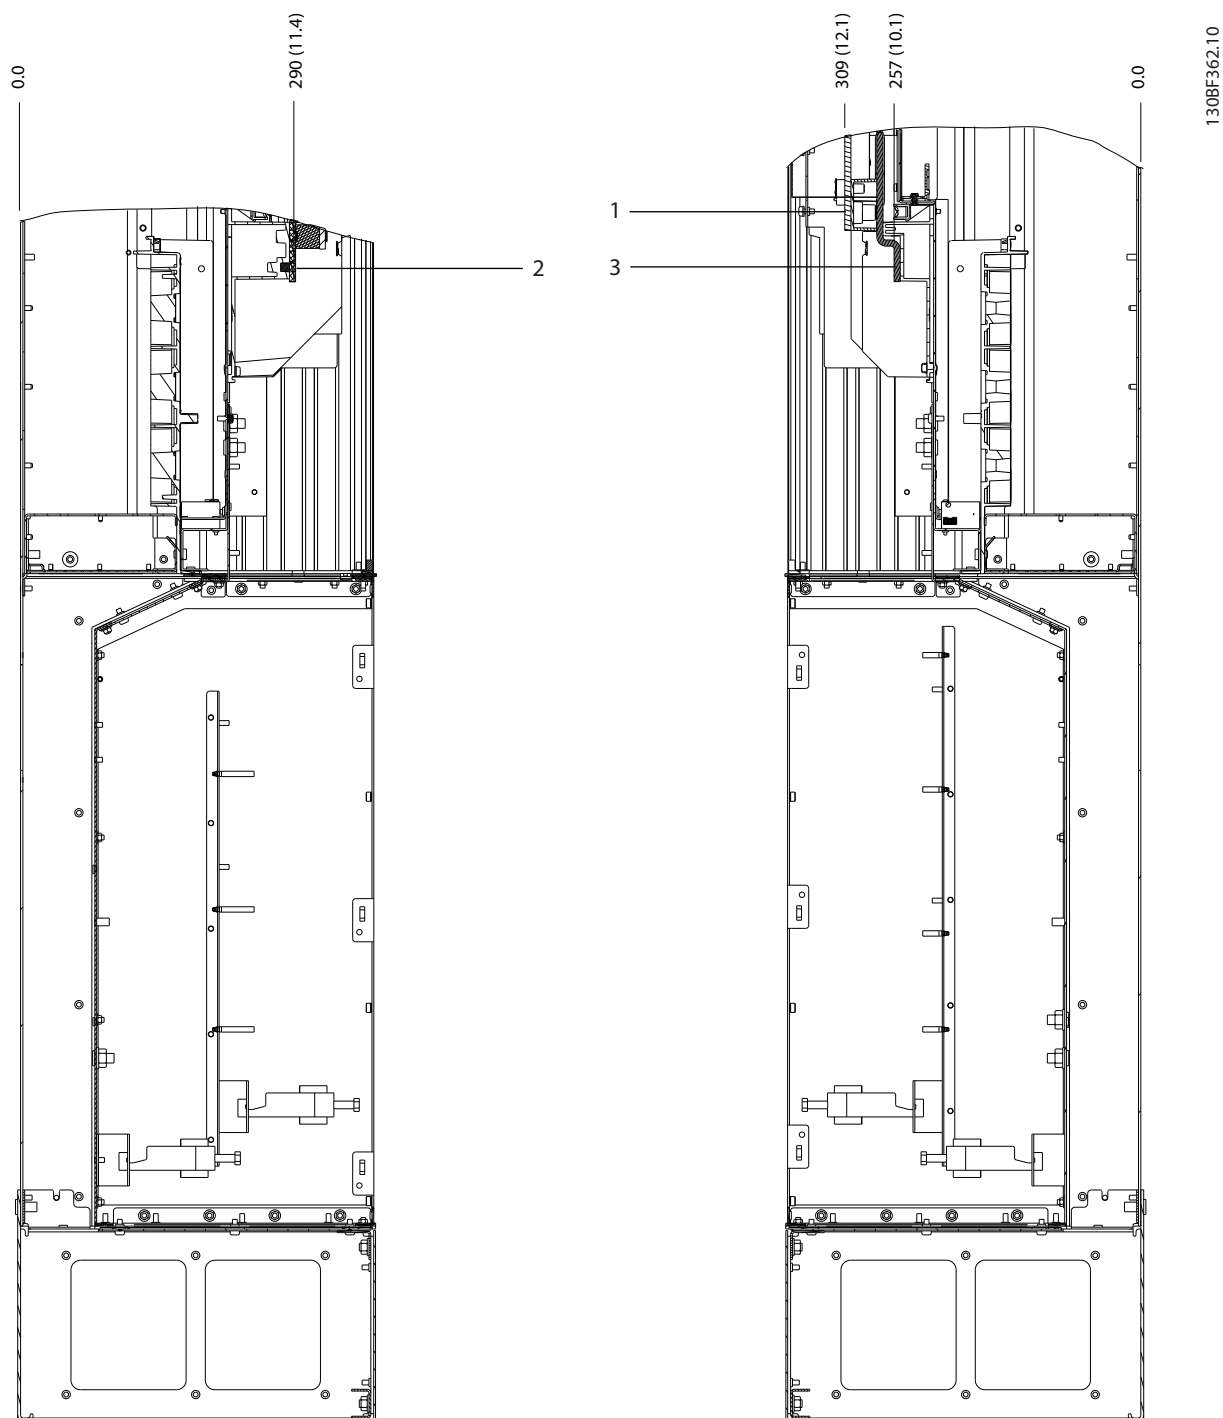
Dimensions des bornes D7h avec option sectionneur (vues latérales)
